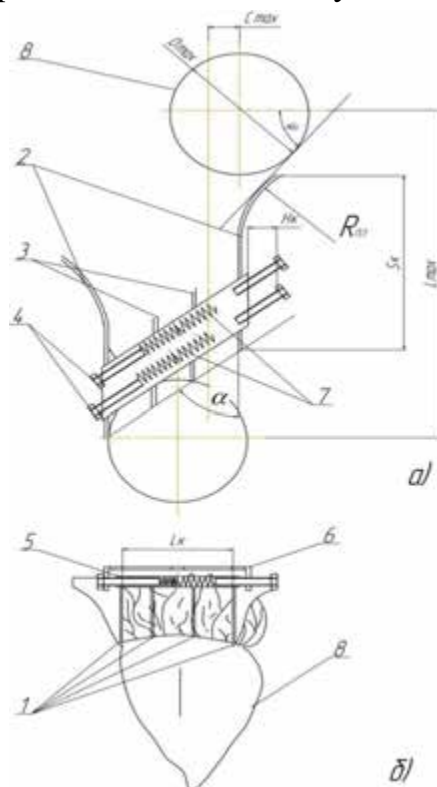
Гребінчастий копір дообрізчика гички: а) – вид зверху; б) – вид прямо; 1 – пластини; 2 – крайня пластинка; 3 – середня пластинка; 4 – направляючий палець; 5 – напрямна втулка; 6 - П-подібна рамка; 7 – пружина; 8 – коренеплід
